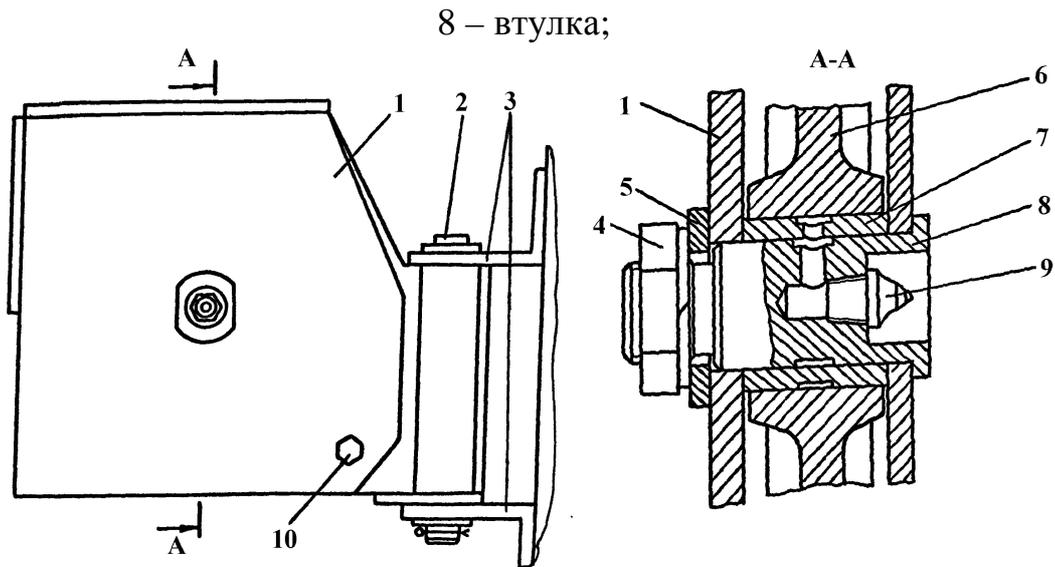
Нижний канатонаправляющий блок: 1 – корпус; 2 – палец; 3 – проушина; 4 – гайка; 5 – шайба; 6 – ролик; 7 – втулка; 8 – ось; 9 – масленка; 10 – болт
